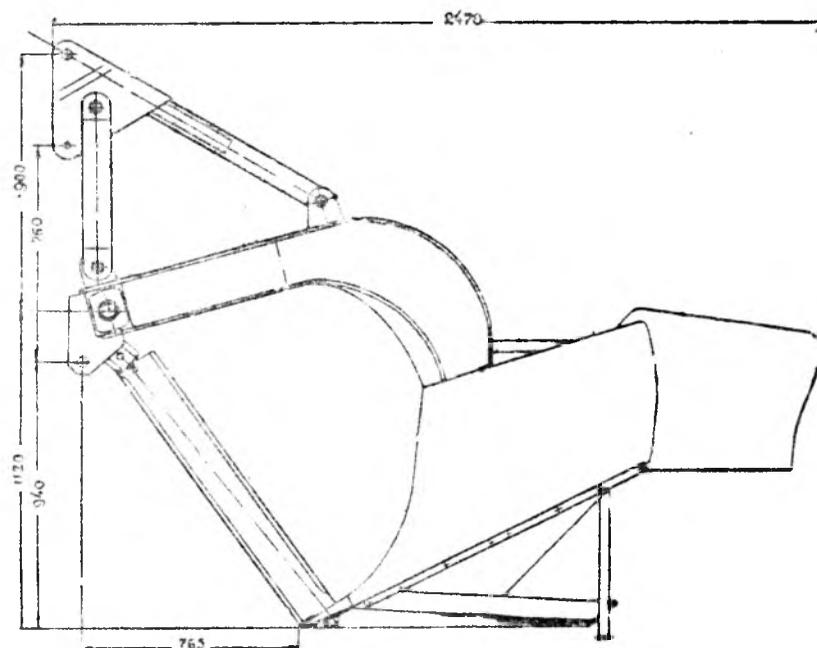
Схема плуга ПКНЛ-500А (вид сбоку)
